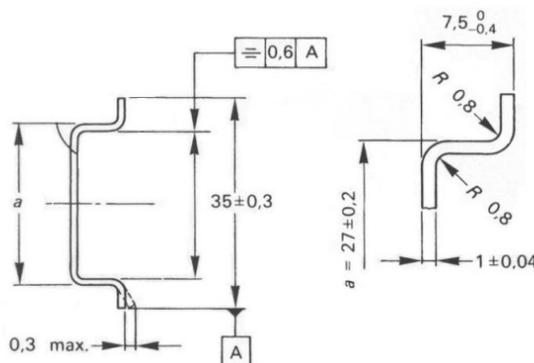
Dimensões (mm) das calhas metálicas de perfil normalizado do tipo TH 35-7.5
